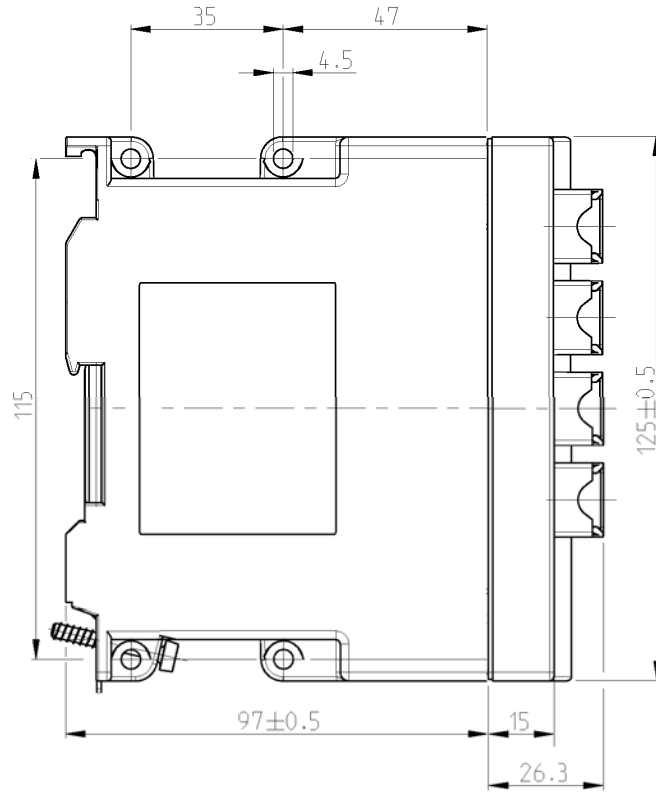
Maßzeichnung X-100 Seitenansicht
